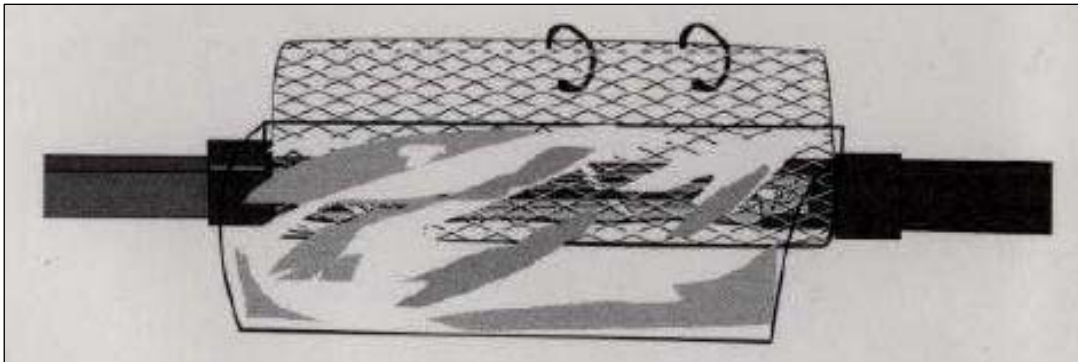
Colocación De La Rejilla Y Cubierta Nylon
